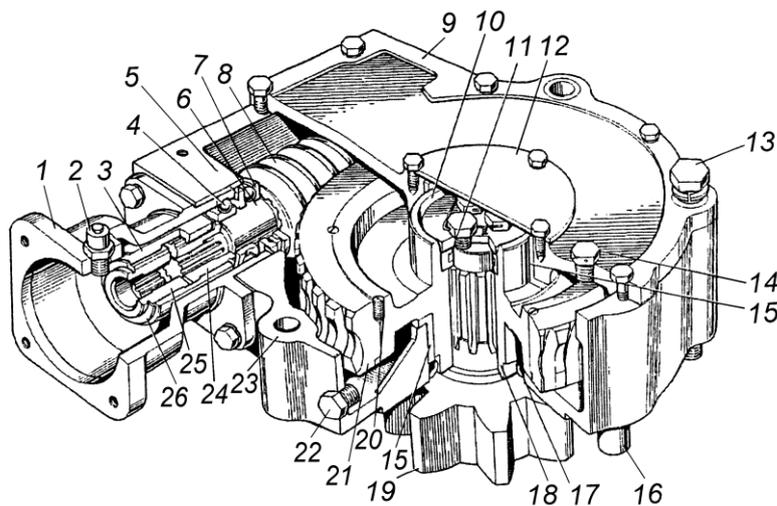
Редуктор поворота отвала: 1 – проставка; 2 – сапун; 3 – шлицевая муфта; 4 – подшипник; 5 – дистанционное кольцо; 6 – вал червяка; 7 – упорный подшипник; 8 – червяк; 9 – крышка корпуса редуктора; 10 – упорная шайба; 11 – уплотнительное кольцо; 12 – крышка; 13 – болт крепления редуктора к тяговой раме; 14 – пробка заливного отверстия; 15 – бронзовая втулка; 16 – установочный палец; 17 – манжета; 18 – ступица червячного колеса; 19 – вал-шестерня; 20 – стопорный винт; 21 – червячное колесо; 22 – пробка сливного отверстия; 23 – корпус редуктора; 24 – шлицевая втулка вала червяка; 25 – шлицевая втулка вала гидромотора; 26 – стопорное кольцо
